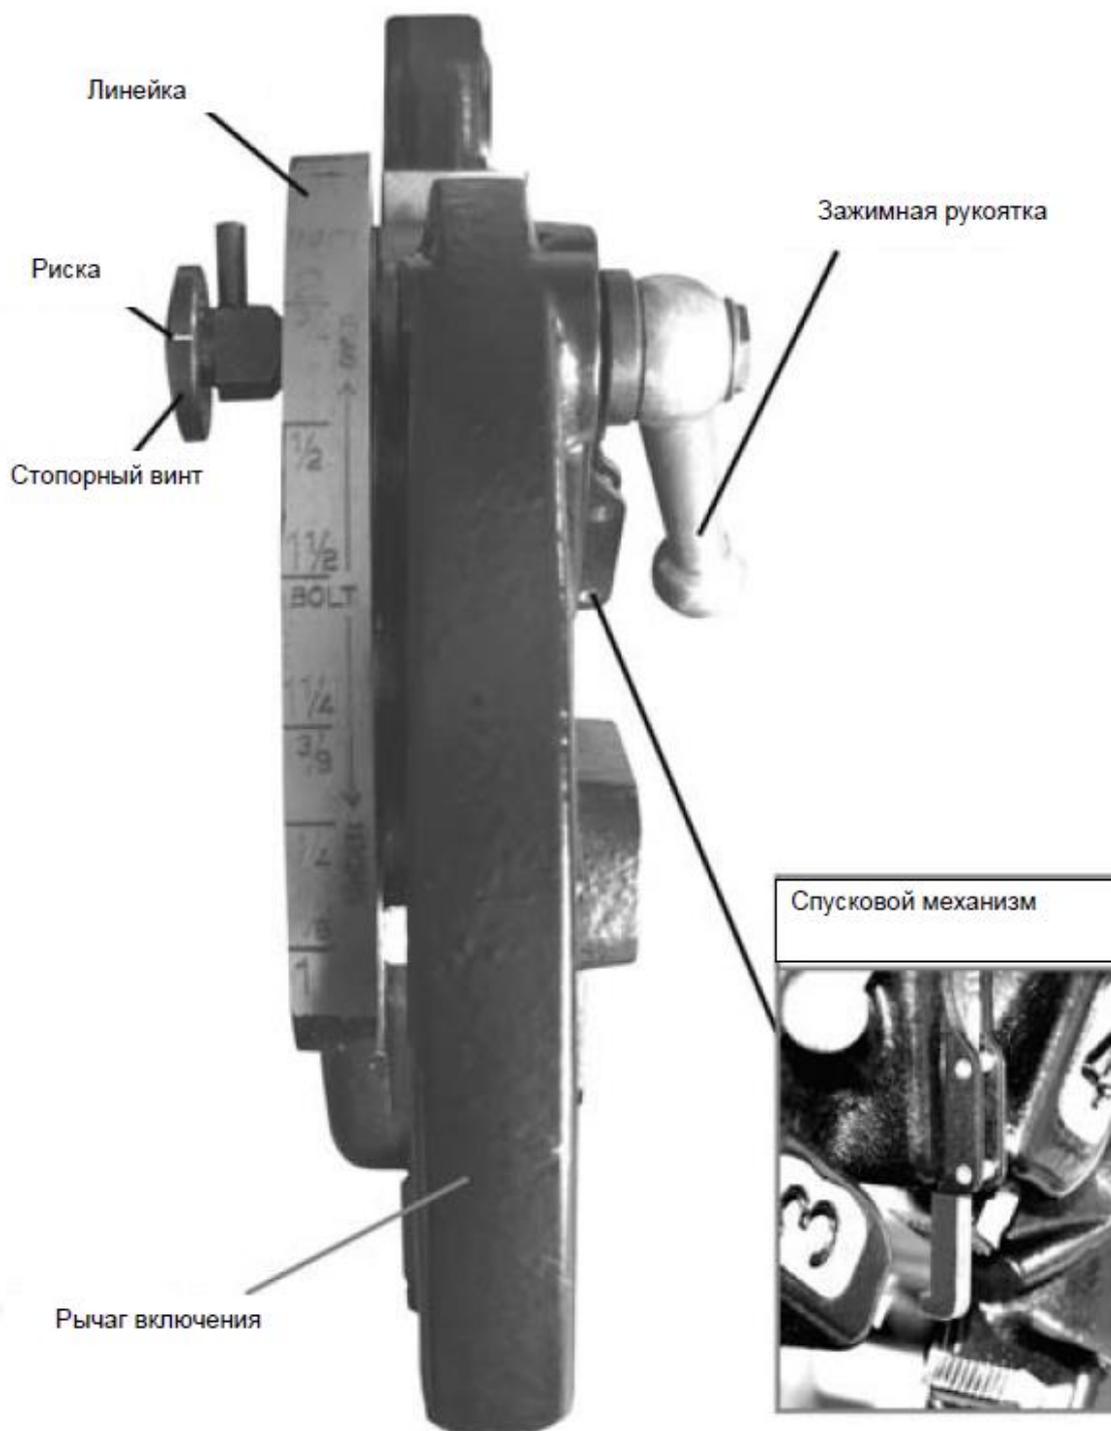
Установка резьбонарезных ножей 1/2"-2"
